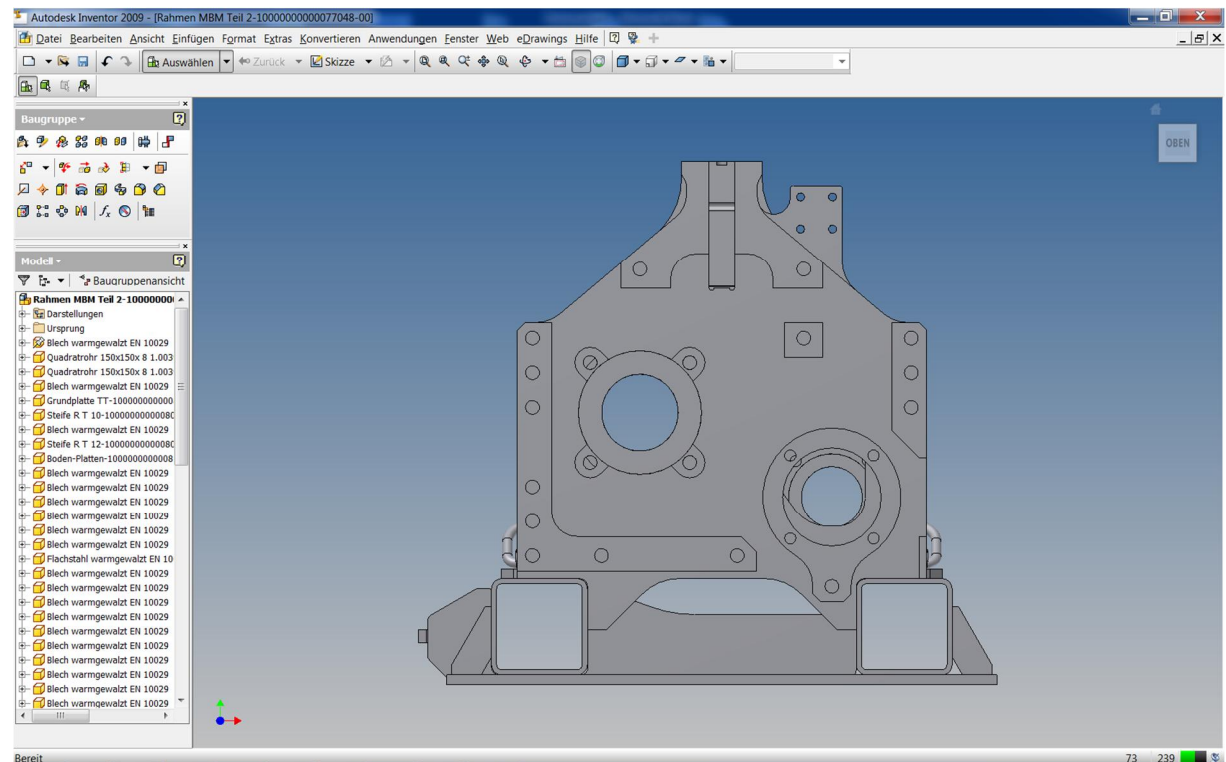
Querschnitt des Grundrahmens der Biegemaschine
